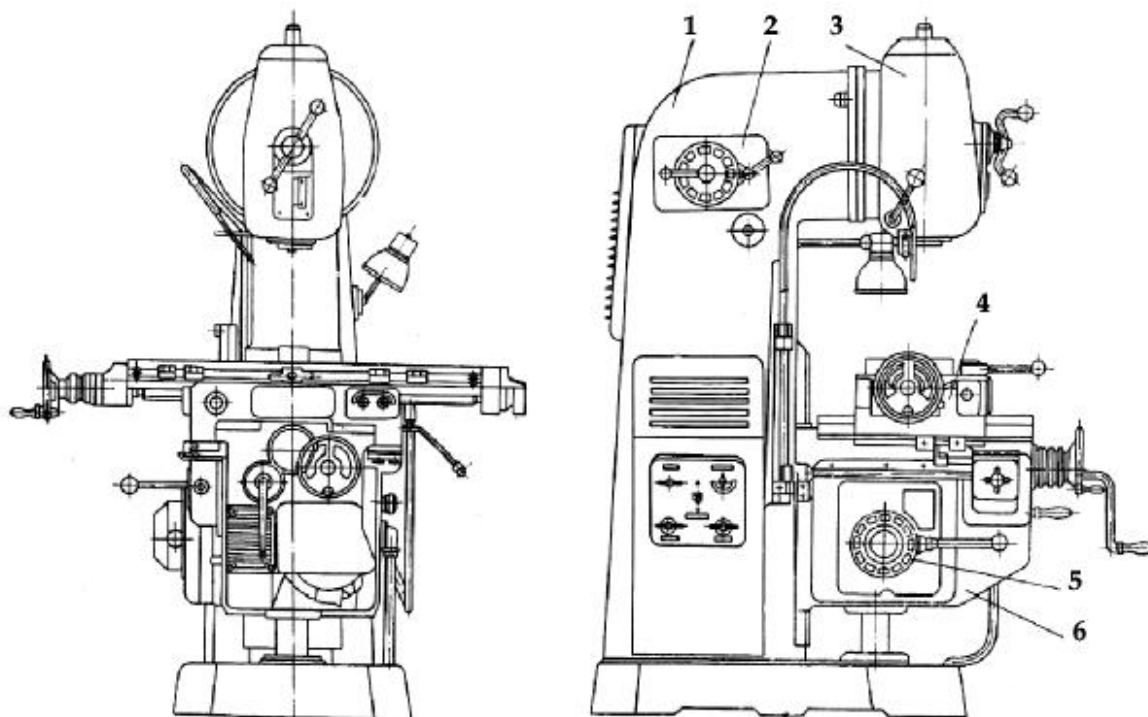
Вертикально-фрезерний верстат: 1 – станина; 2 – коробка швидкостей; 3 – шпindelна головка; 4 – стіл; 5 – коробка подач; 6 - консоль
